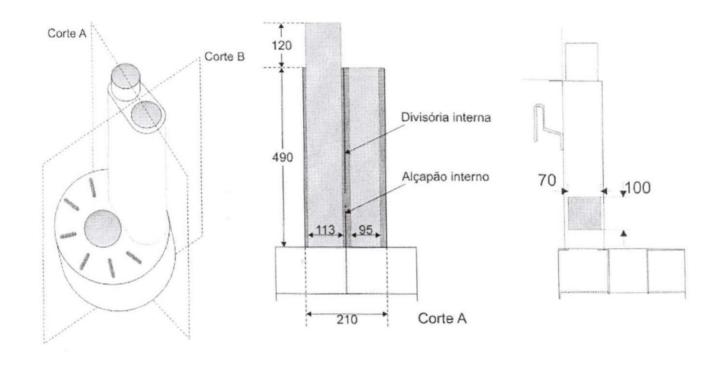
Vista em perspectiva do aquecedor (Corte A e B)
